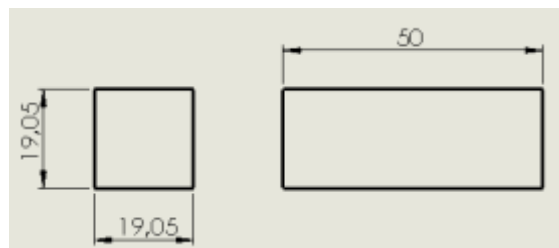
1. Dimensiones de los electrodos de sección cuadrada (mm).
